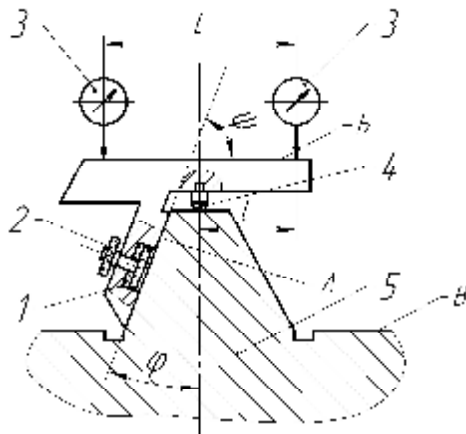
Устройство для контроля величины угла наклона боковой поверхности призмы направляющей станины станка: 1 – корпус; 2 – магнит; 3 – индикатор часового типа; 4 – опора; 5 – станина; А – контролируемая боковая сторона призмы; В – контрольная плоскость устройства; В – плоскость направляющей станины; L – расстояние, на которое перемещается индикатор часового типа; φ – контролируемый угол призмы; I – I – ось призмы; ψ – угол между плоскостями А и В
